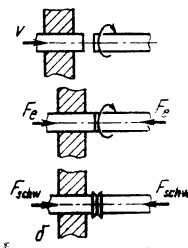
Принцип сварки: а — схема; б — эскиз ( $F_{Schw}$  — давление при сварке)
